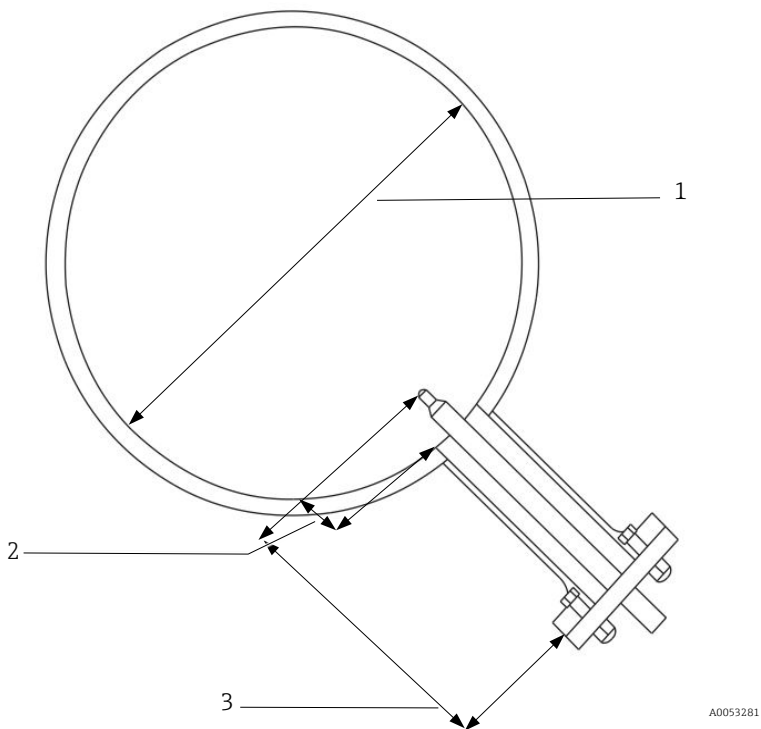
Parâmetros de instalação da sonda Rxn-41 para bunkering de GNL
